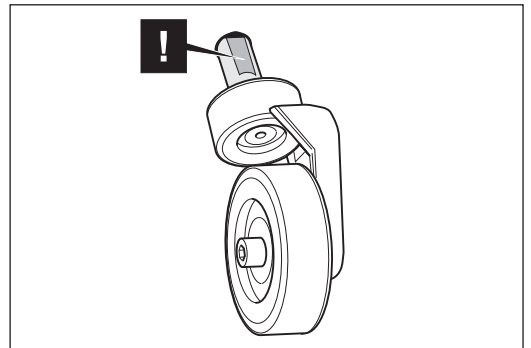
Beim Einbau des Hinterrads in die Maschine die Fläche der Spornachse zur Schraube im Maschinengehäuse ausrichten.
